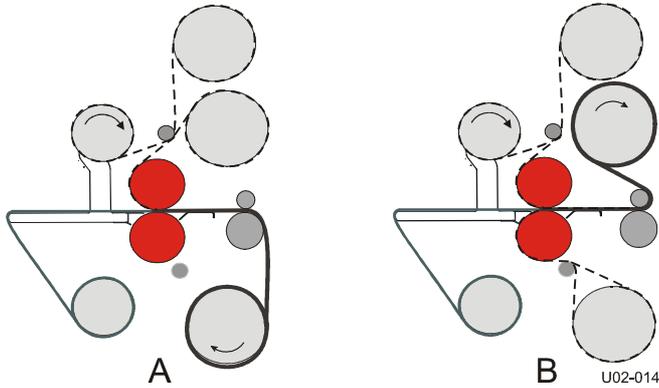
Rolle-zu-Rolle Arbeitsverfahren mit eingerückten Zugwalzen
